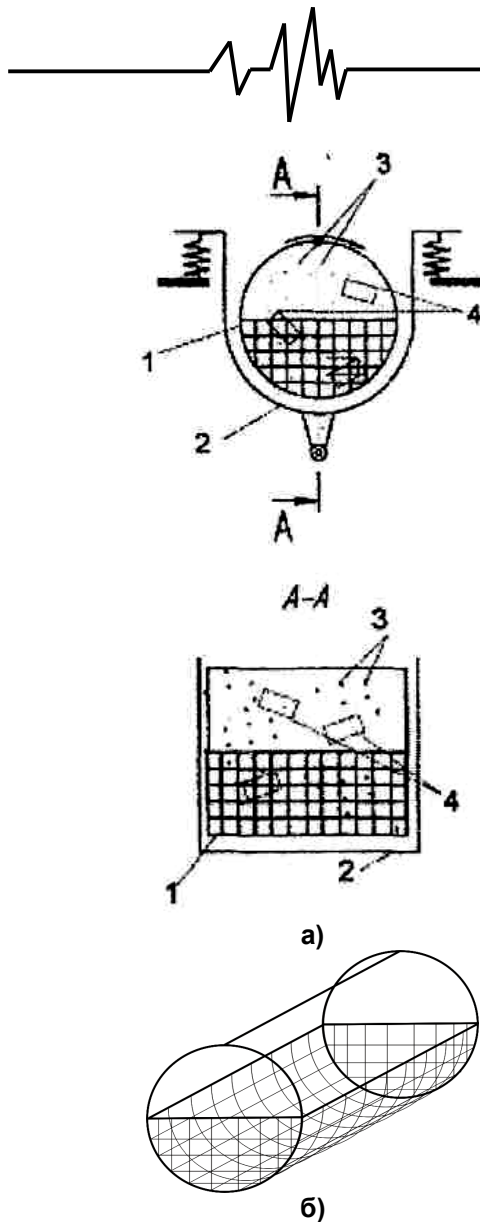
Конструкции вибрационного станка с разгрузочно-разделительным устройством (а) и внешний вид данного устройства (б)
